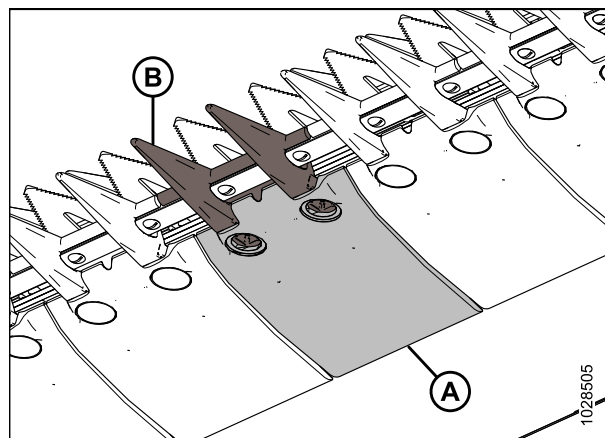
Центральный противорежущий палец и износная пластина
